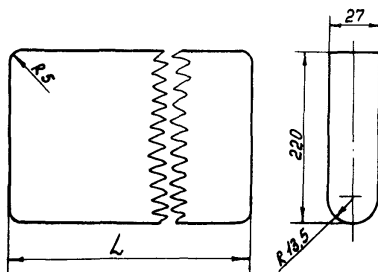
Подвесное приспособление для подвески катушек (а) и схема расположения отверстий под крышки (б)
